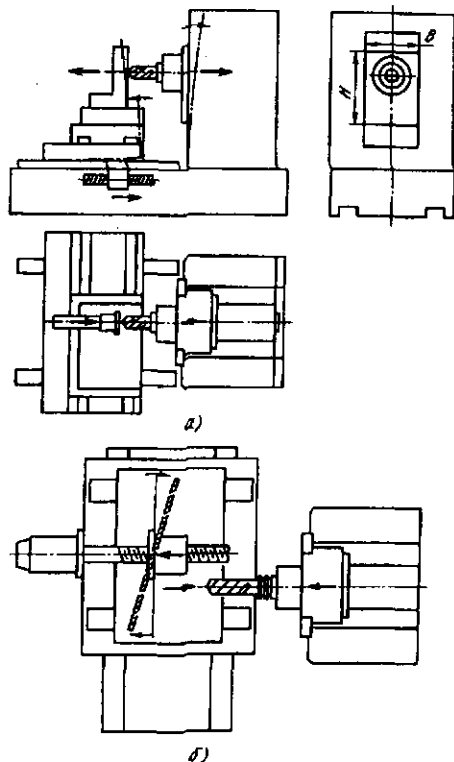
Компоновка станка с ЧПУ с арочной конструкцией колонны с центральным (а) и смещенным (б) расположением ходового винта привода поперечной подачи стола
